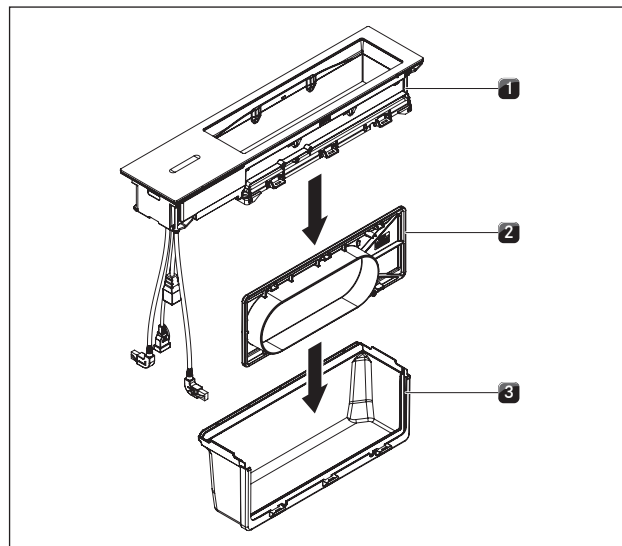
Geassembleerde kookveldafzuiging CKA2
